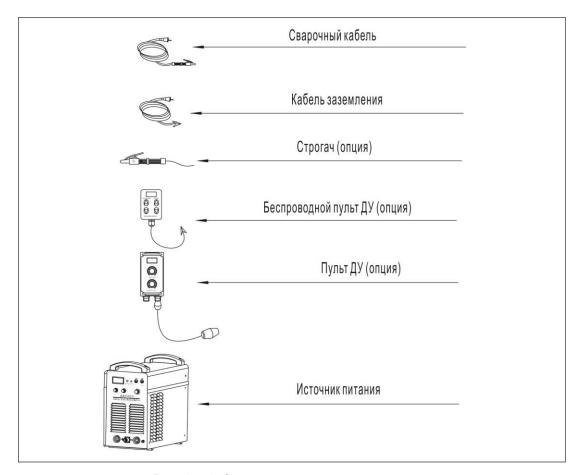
Основные элементы сварочной системы
